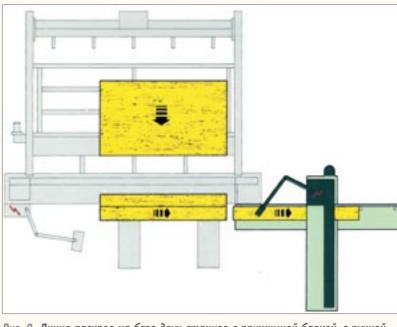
Линия раскроя на базе двух станков с прижимной балкой, с ручной передачей полос между станками
